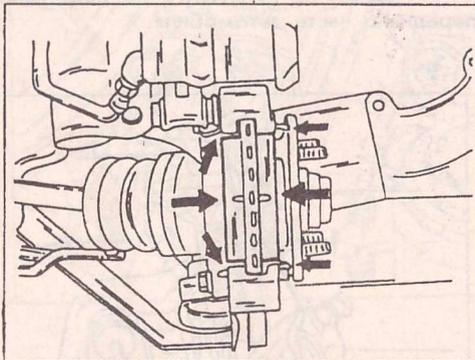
Схема сборки суппорта. Показанные в правой части рисунка детали устанавливаются на автомобилях с двигателями большей мощности.
